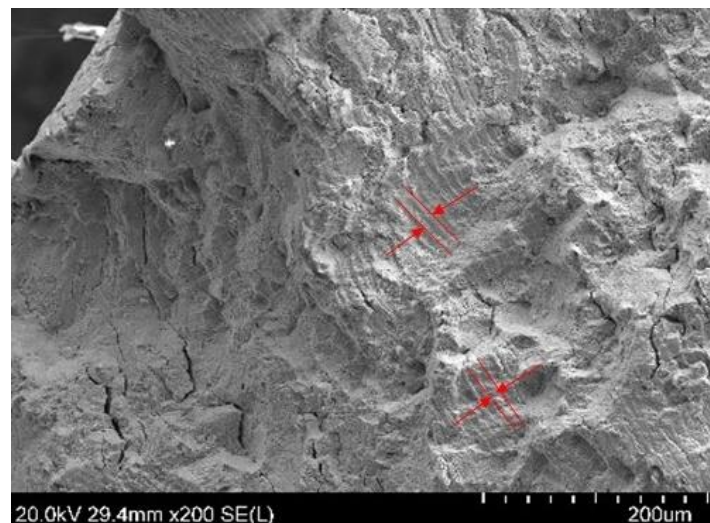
Мелкие усталостные бороздки вблизи очага разрушения тонкостенного образца с технологической шероховатостью поверхности
